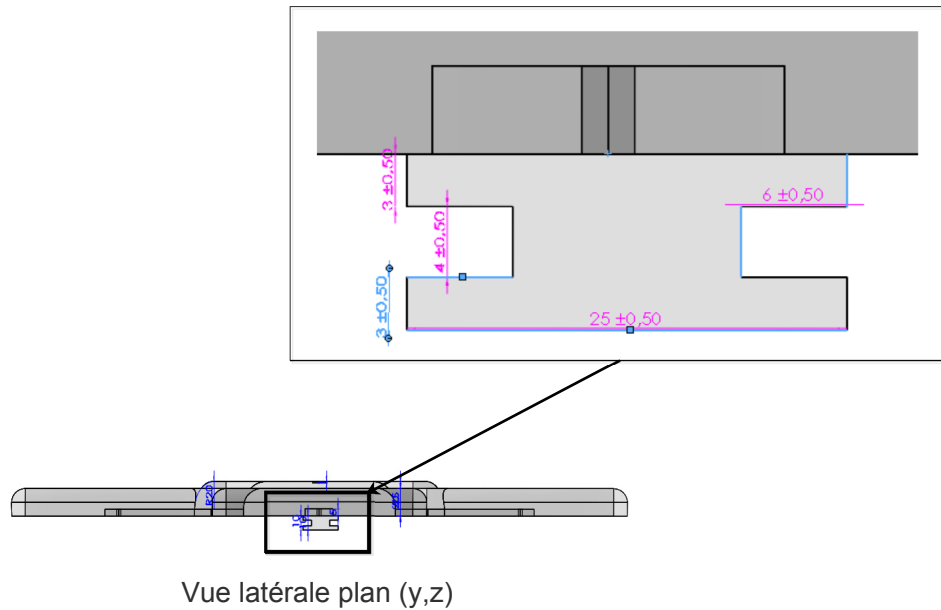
Dimensions de l'élément de base de la glissière.
